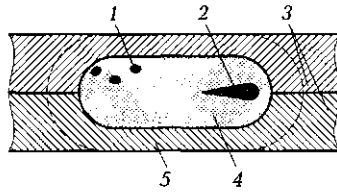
Сварное соединение с порами и усадочной раковинной, выполненное точечной контактной сваркой:
